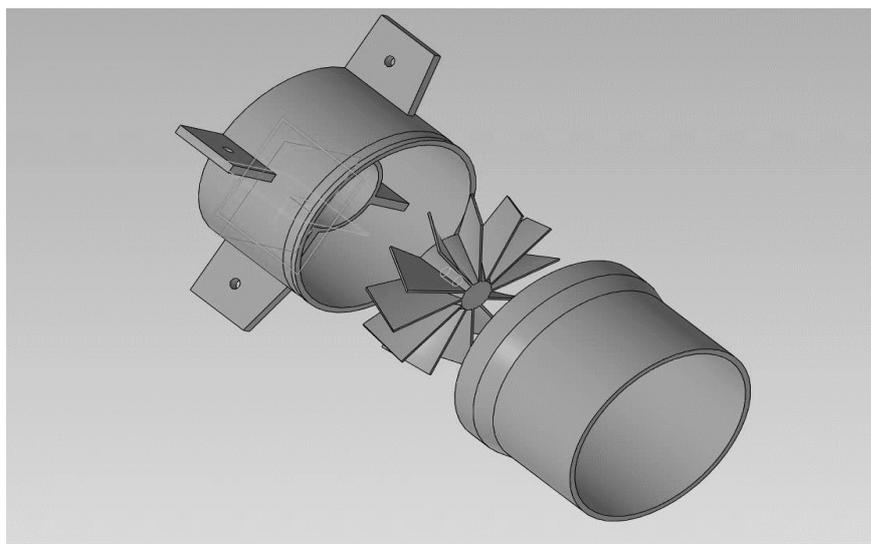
Основная модель кожуха, крыльчатки и корпуса
